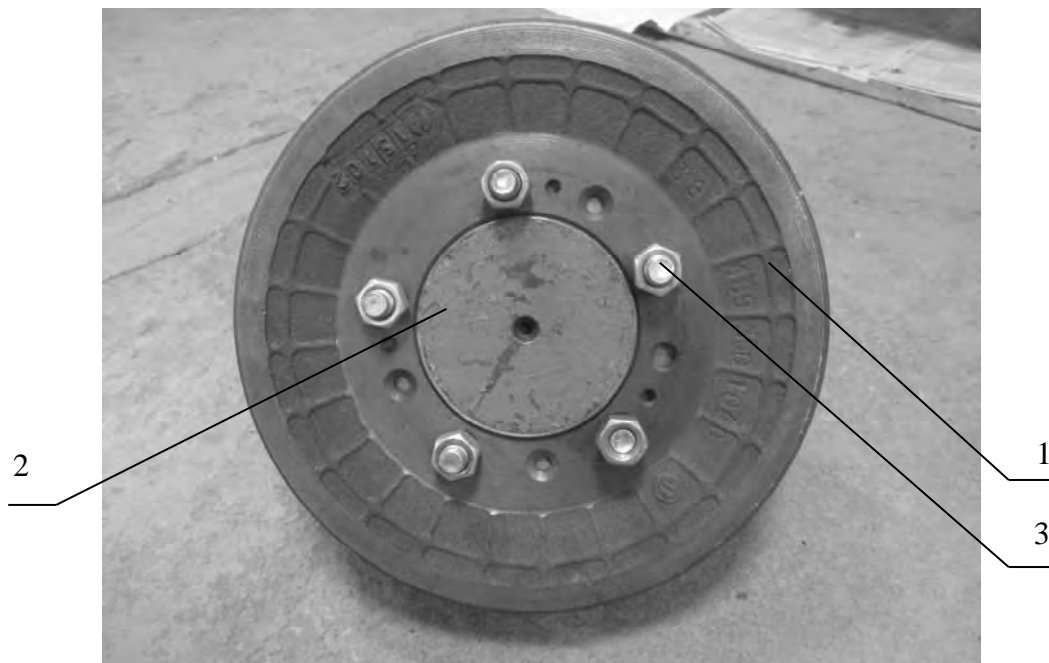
Размещение тормозного барабана относительно фланца полуоси бортового редуктора: 1 – тормозной барабан; 2 – фланец полуоси; 3 – болты крепления тормозного барабана к фланцу полуоси
